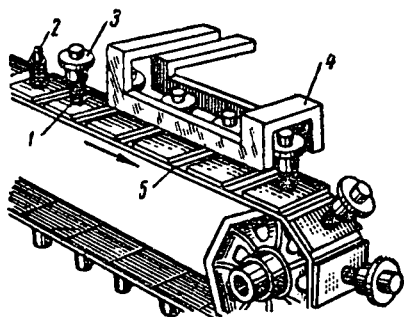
Автомат для высокочастотного паяния с непрерывной подачей деталей в индуктор
